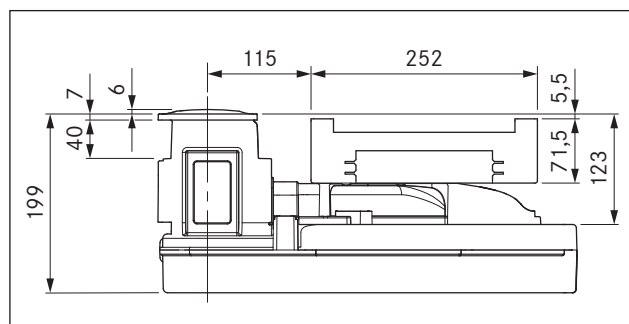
PKAS, PKASAB dimensões do aparelho vista frontal
